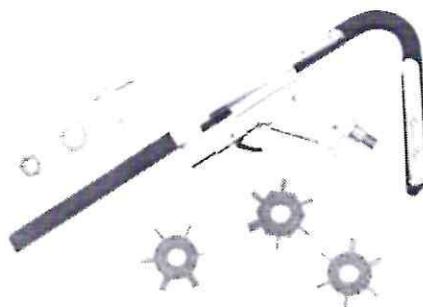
Приспособление для чистки поршневых канавок
